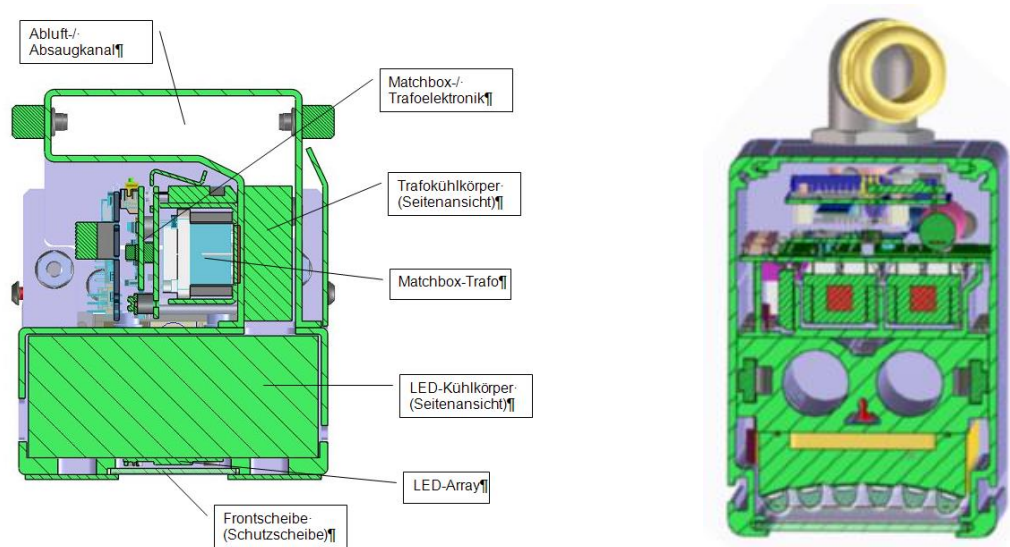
Links: CAD-Zeichnung (Schnitt) des luftgekühlten Aggregates.
